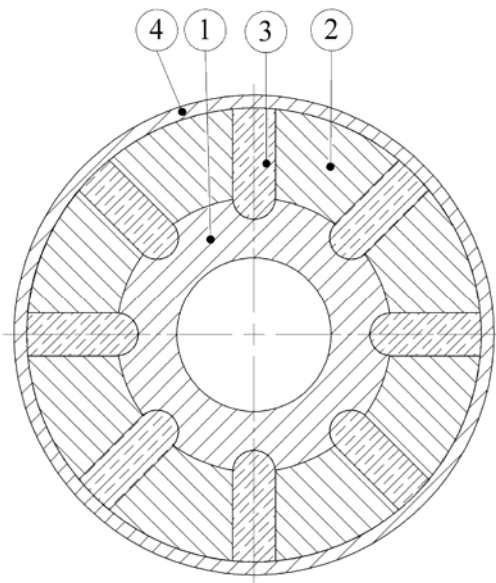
Конструктивная схема ротора с тангенциальным намагничиванием; 1- немагнитный вал; 2-полюс; 3-магнит; 4- немагнитный бандаж.
